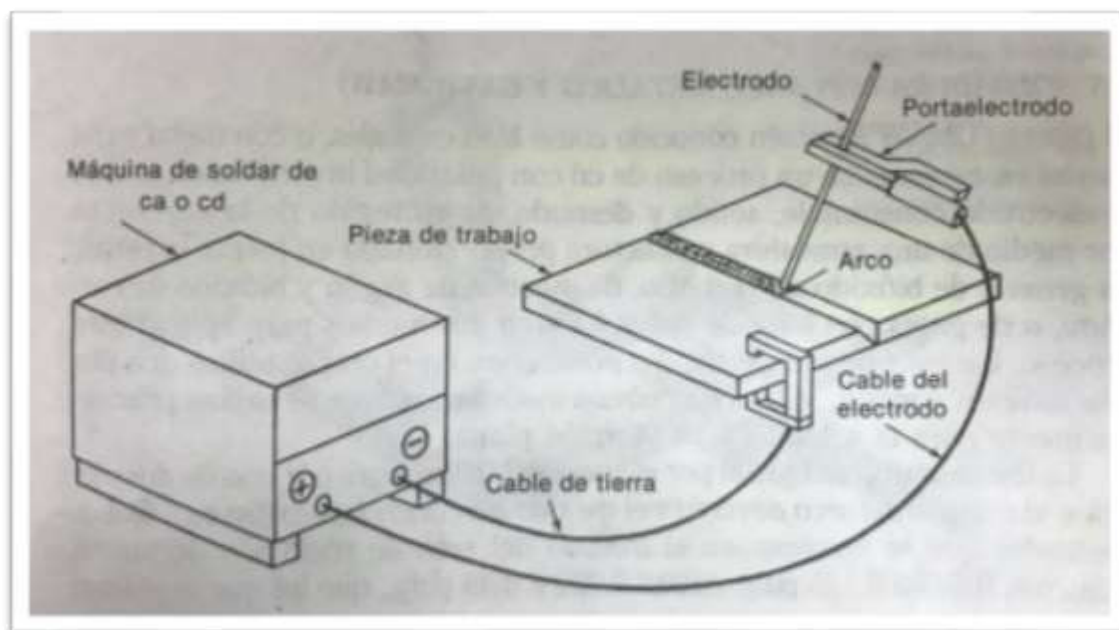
Disposición de los elementos básicos para soldadura SMAW (Fuente: Soldadura Aplicaciones y Práctica)
